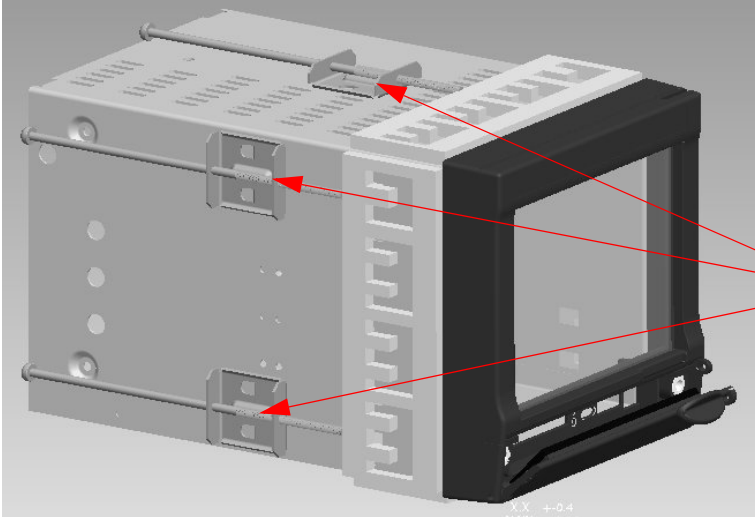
Minitrend GR - Brides de fixation pour panneau de 45 mm d'épaisseur
